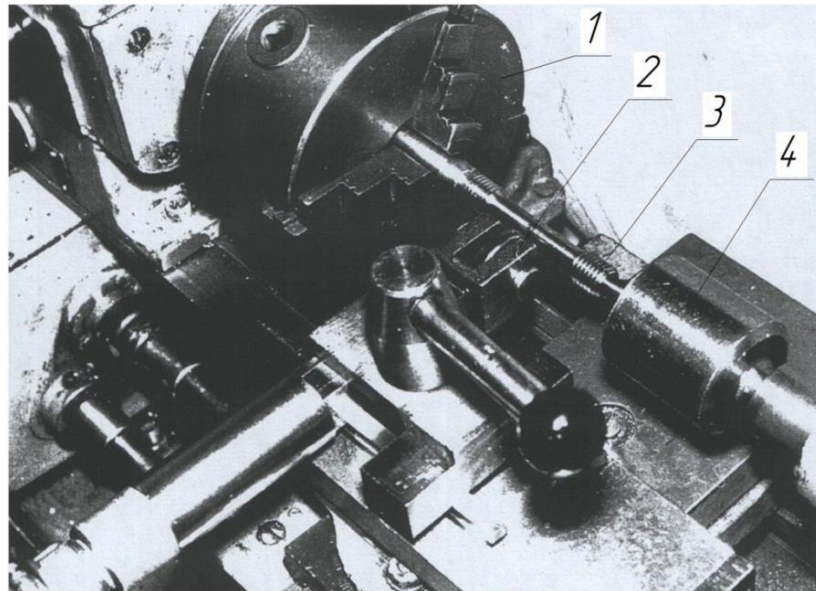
Загальний закріплення циліндричного металевго зразка на токарному верстаті 16К20 для операції ініціювання кільцевої тріщини: 1 - верстат токарний; 2 – прилад для поперечного згину металевго зразка; 3 – циліндричний металевий зразок; 4 – центр обертовий.
